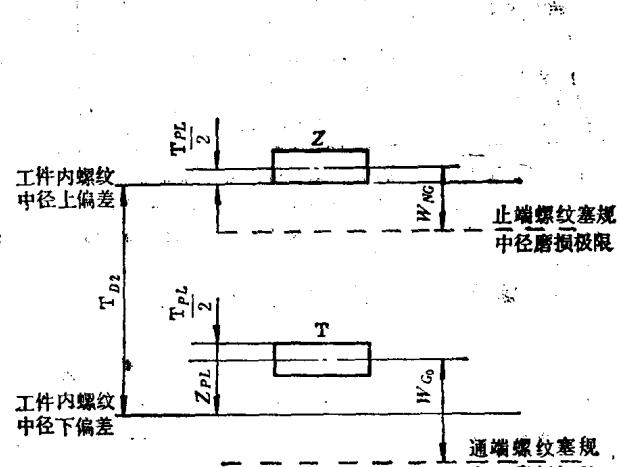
检查工件内螺纹用的螺纹塞规中径公差带图
